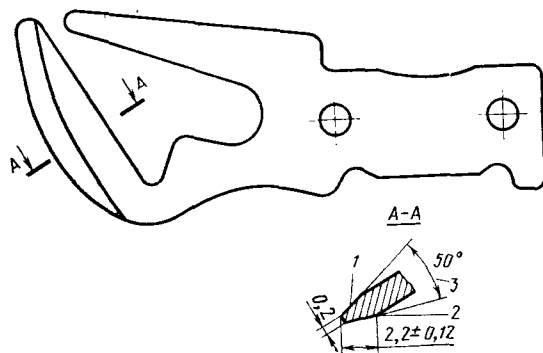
Обработка фасонных поверхностей зуба батана
